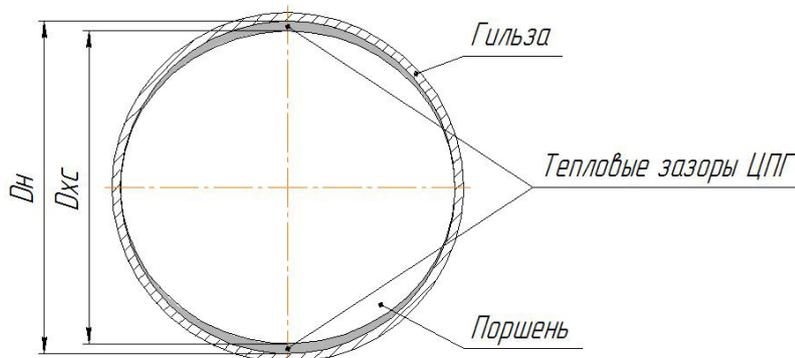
Пояснительная схема обозначения тепловых зазоров цилиндро-поршневой группы
